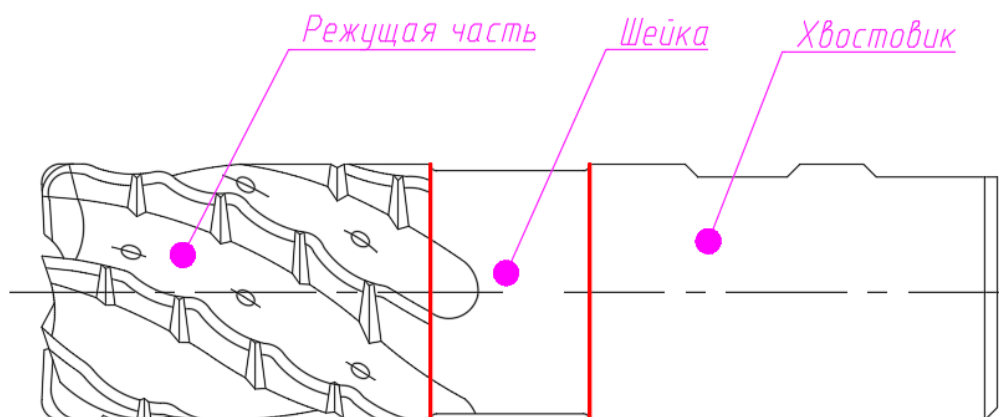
Концевая фреза из порошковой быстрорежущей стали
